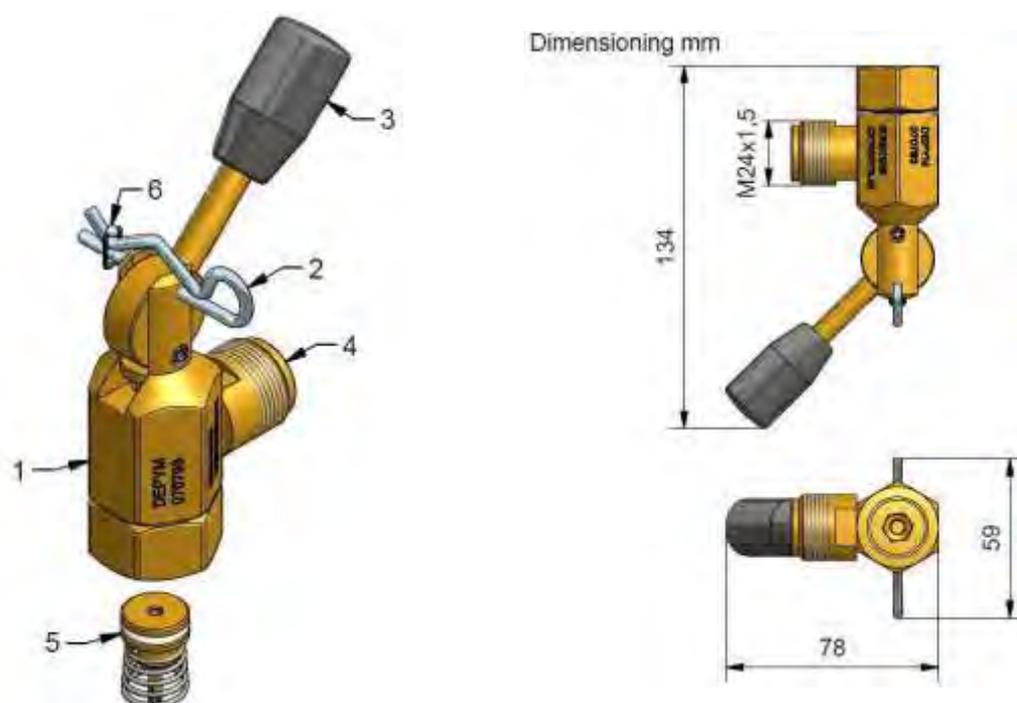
Устройство ручного и пневматического пуска DEPYM
